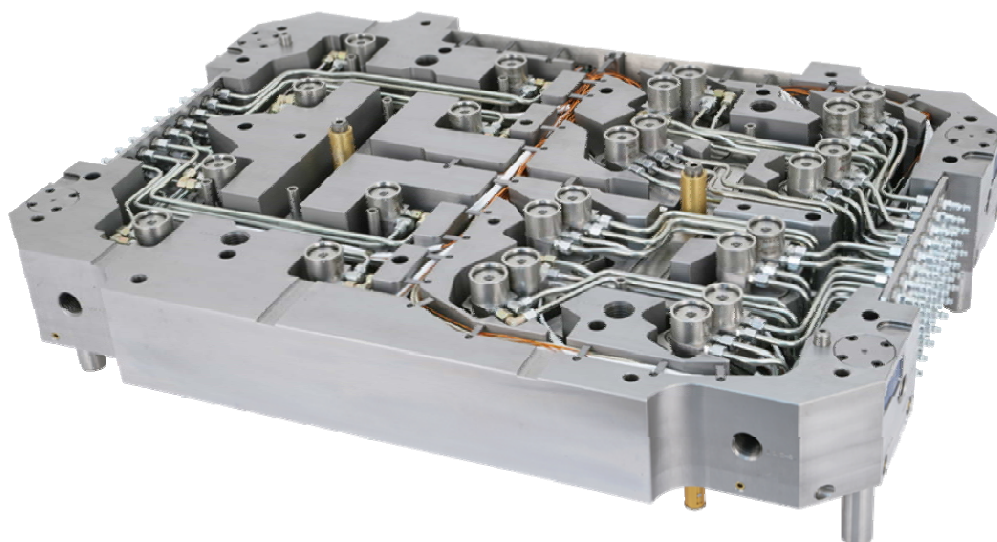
Sistema *Hot Half*, com câmara instalada na parte fixo do molde, pronto para acoplar à parte móvel do molde.
